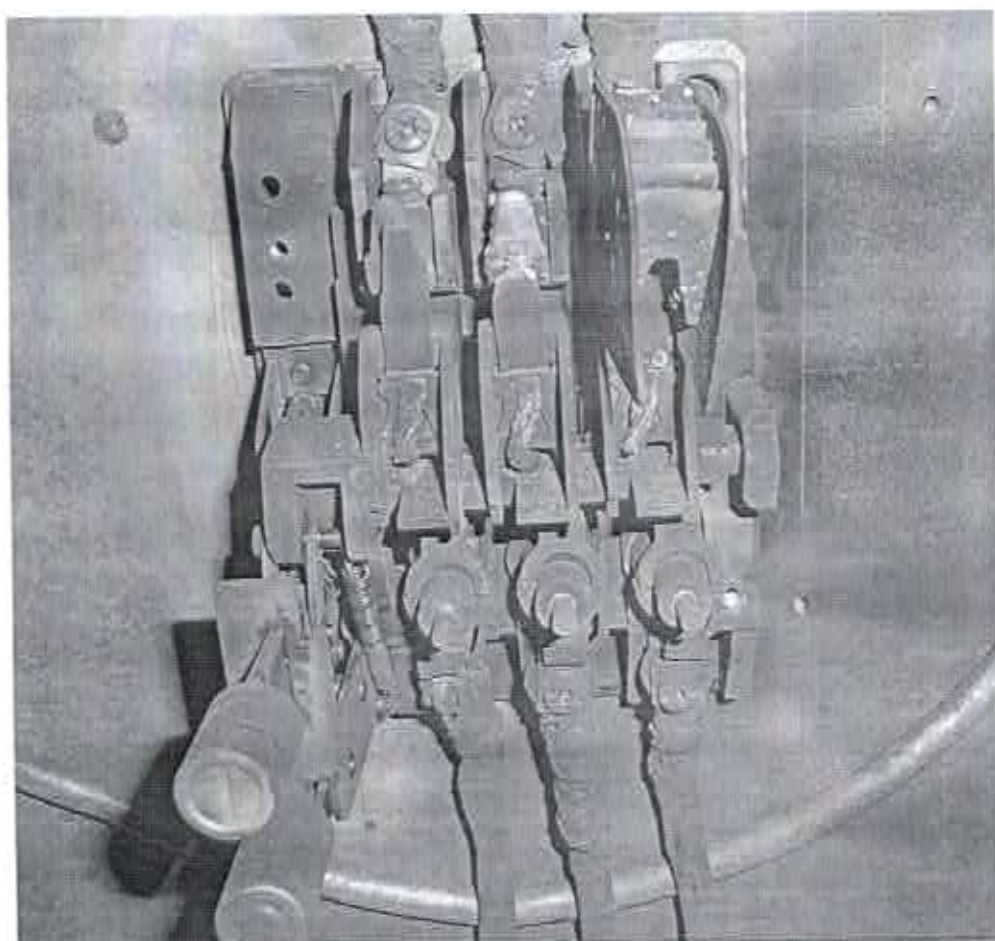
Образец № 1 после испытания на ПКС, вид со снятой крышкой
